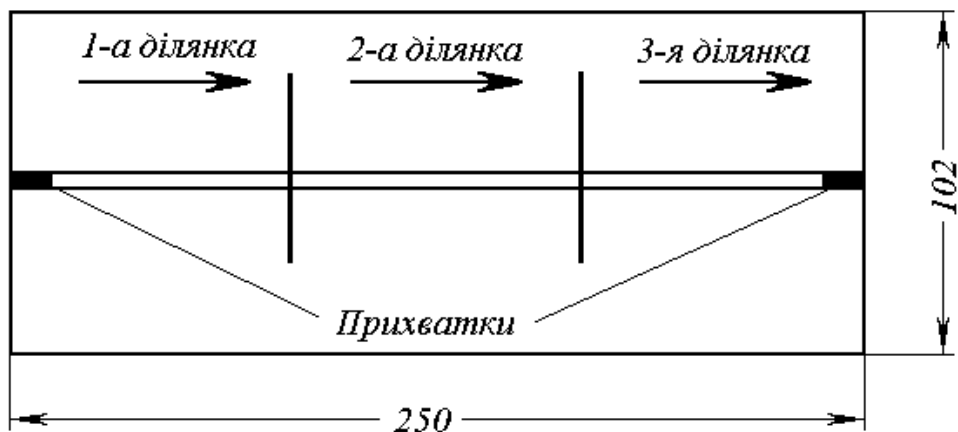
Схема збирання пластин і наплавки валиків
